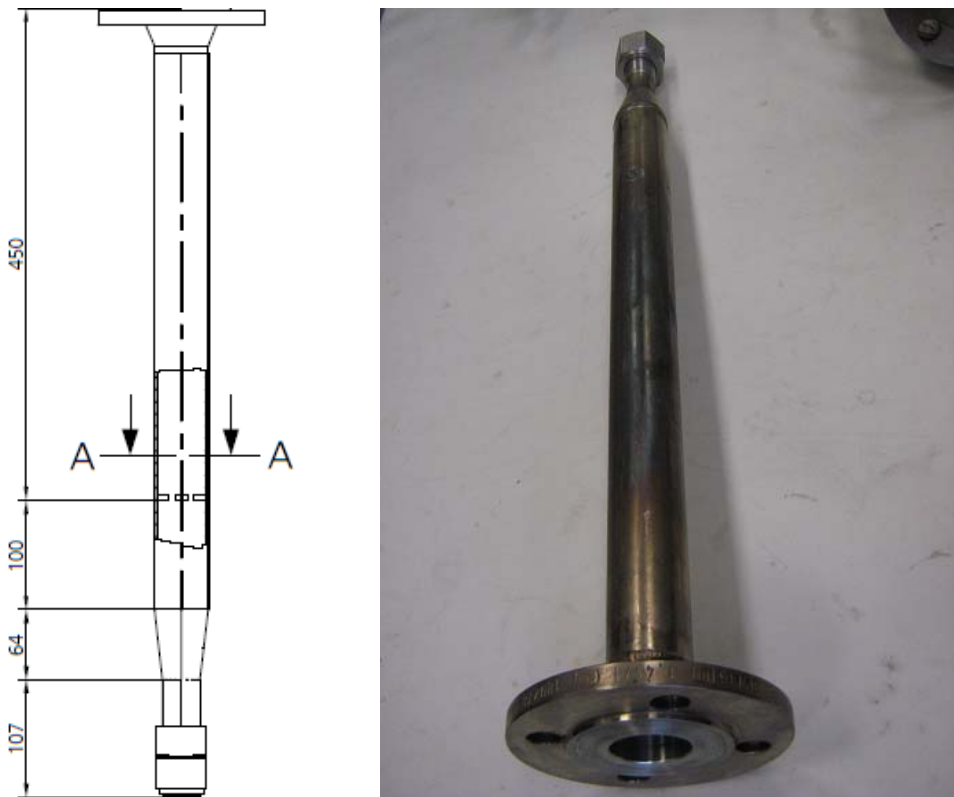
technische Zeichnung (Ausschnitt) des Reaktors sowie Ansicht des fertigen Bauteils
